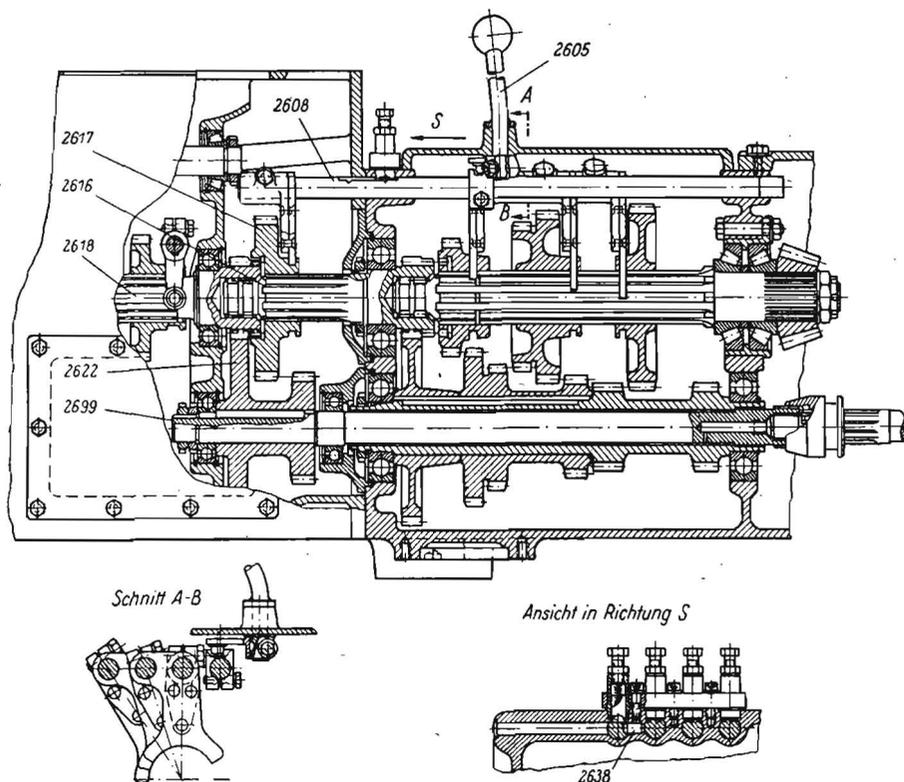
Längsschnitt durch Kupplungs- und Getriebekasten des Radschleppers Zetor Super mit Kriechgang
